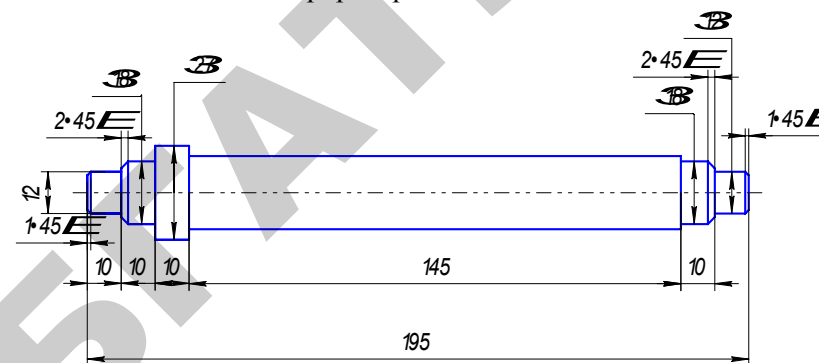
а – Оправка для выпрессовки и запрессовки гнезда перепускного клапана
